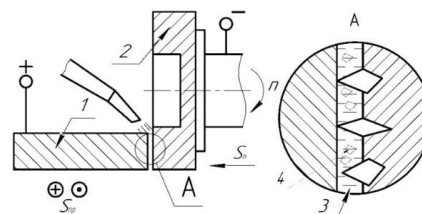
Схема электроалмазной обработки: 1 — заготовка; 2 — связка круга; 3 — электролит в межэлектродном зазоре; 4 — стружка
